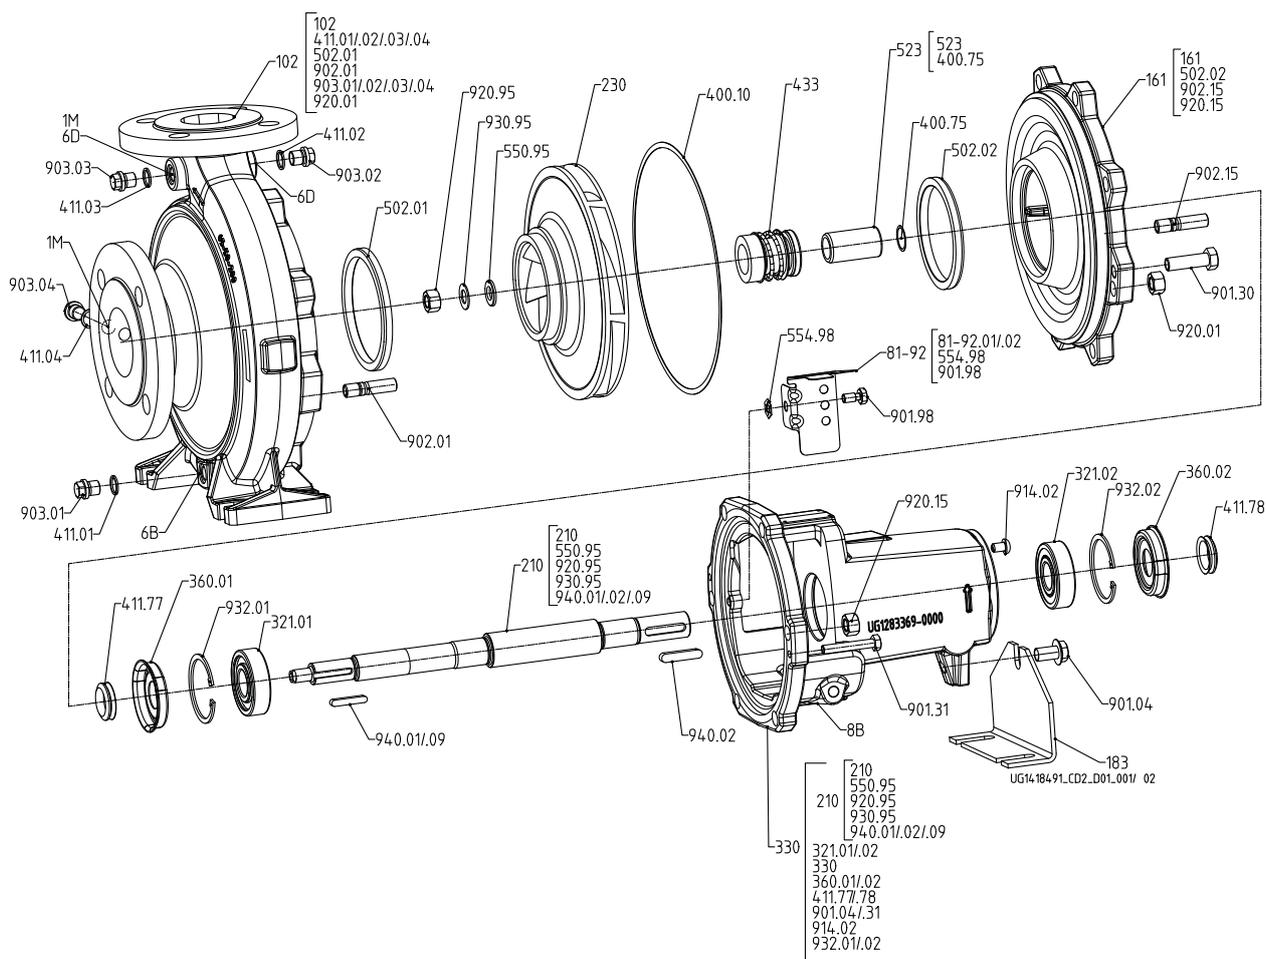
Исполнение со стандартным торцовым уплотнением и привинчиваемой крышкой корпуса
